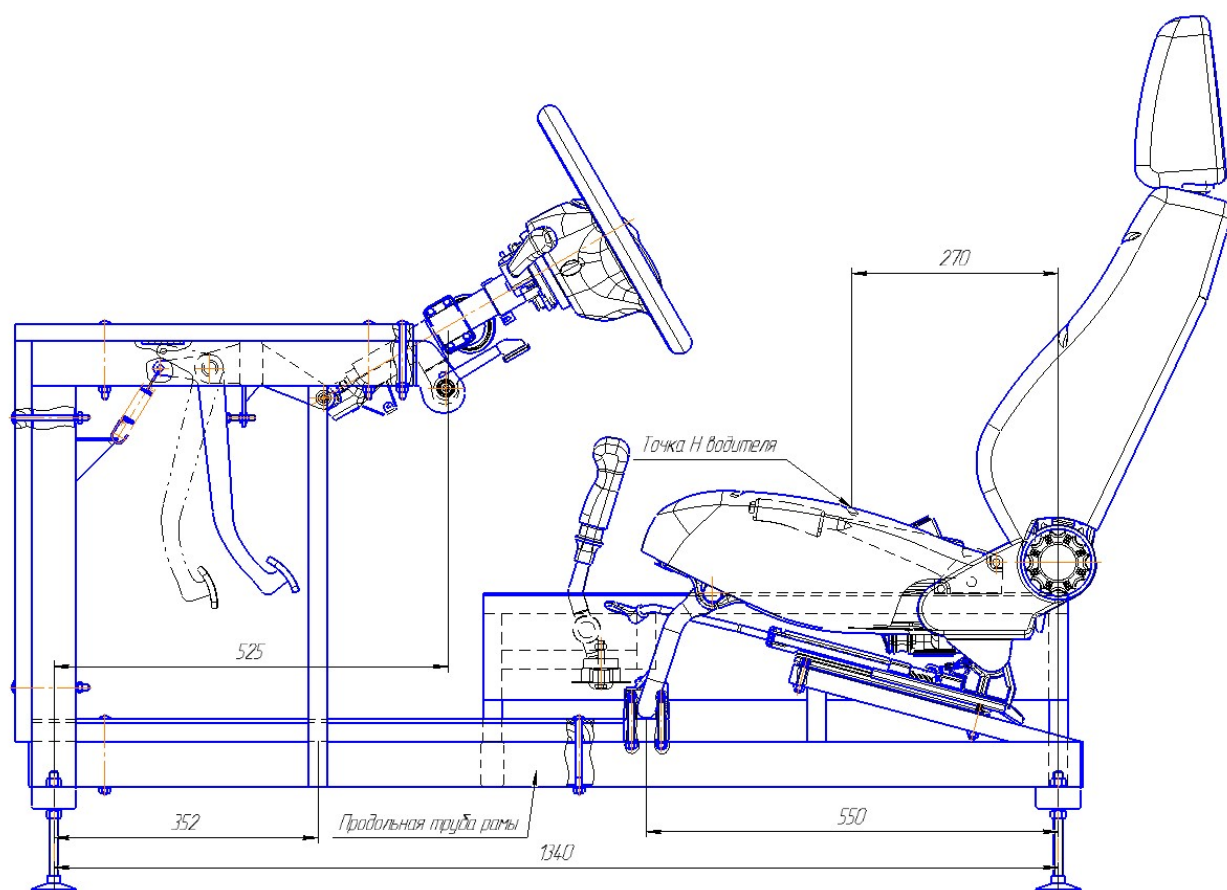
Схема стенда к расчету продольных труб рамы
